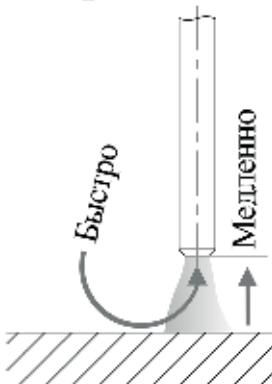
Способы зажигания сварочной дуги.
